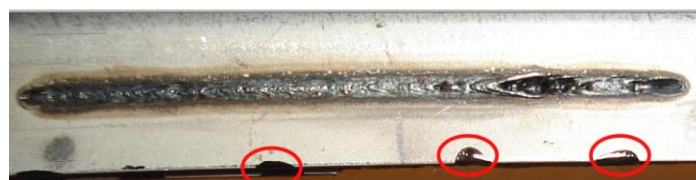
Segmento con soldadura del ensamble mostrado en la Figura 2(b), que muestra no uniformidades en el borde.
